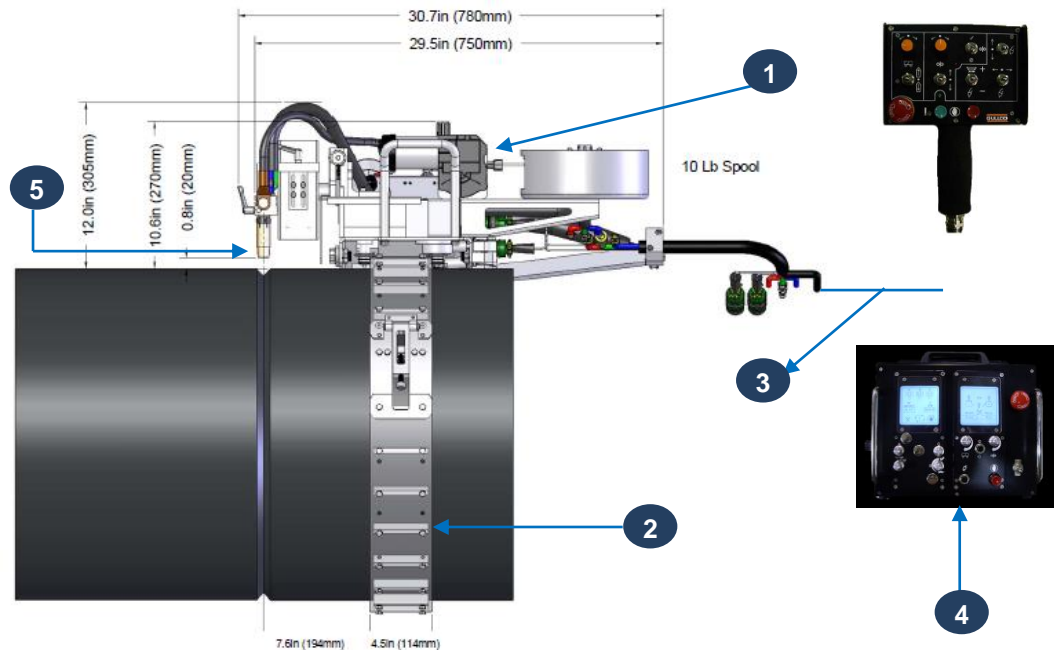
Soldagem Mecanizada – Sistema Orbital
